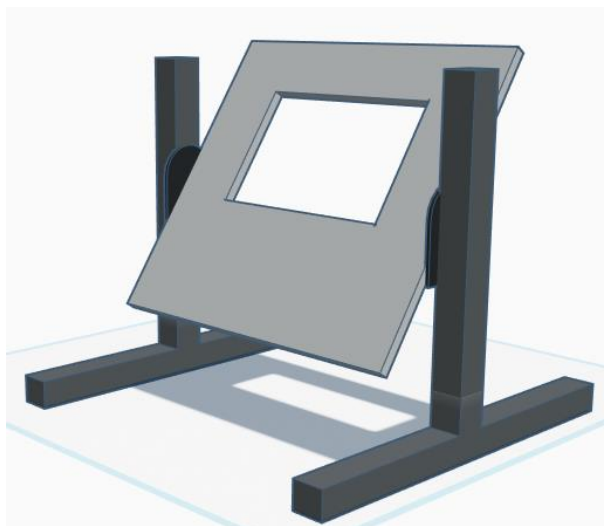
Prototipo 3D del diseño final (Fuente: propia)
